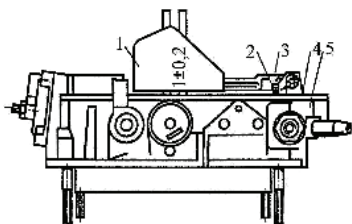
Установка уровня топлива в поплавковой камере карбюратора типа «Солекс»
